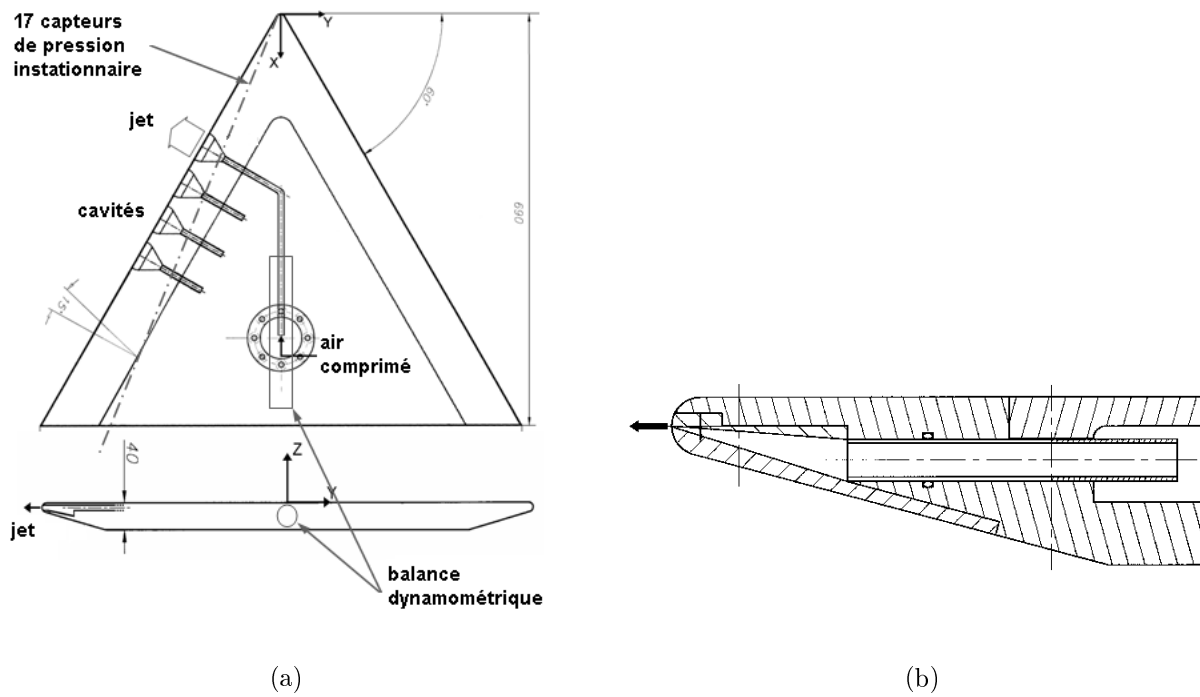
Vue d'ensemble des moyens de contrôle et de mesure sur la maquette modulaire (a) et vue en coupe d'une cavité de soufflage (b)
